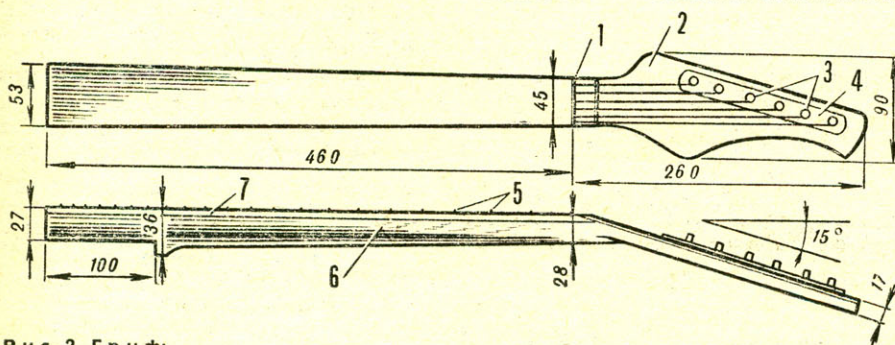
Гриф: 1 — верхний порожек; 2 — головка грифа; 3 — колки; 4 — декоративный пластик; 5 — лады; 6 — гриф; 7 — накладка.
